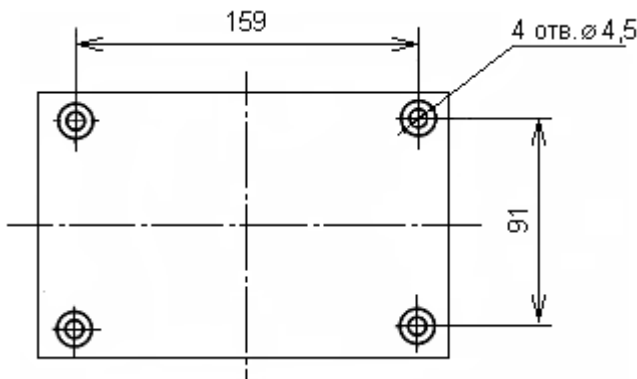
Крепление адресного блока (присоединительные размеры)
